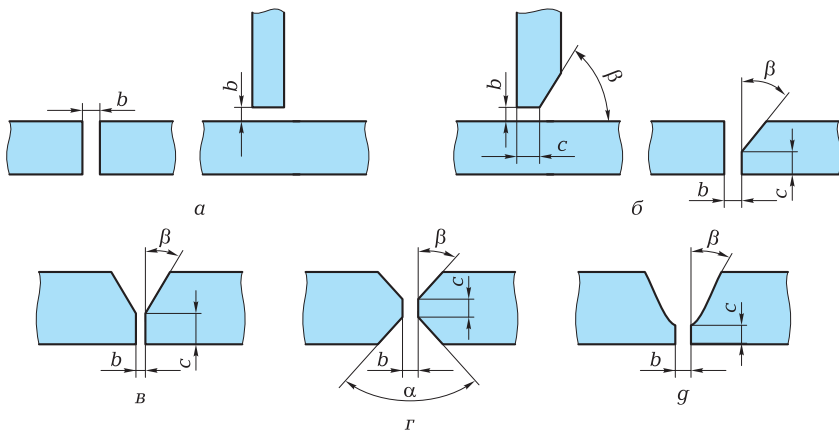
Конструктивные элементы разделки кромок под сварку:
